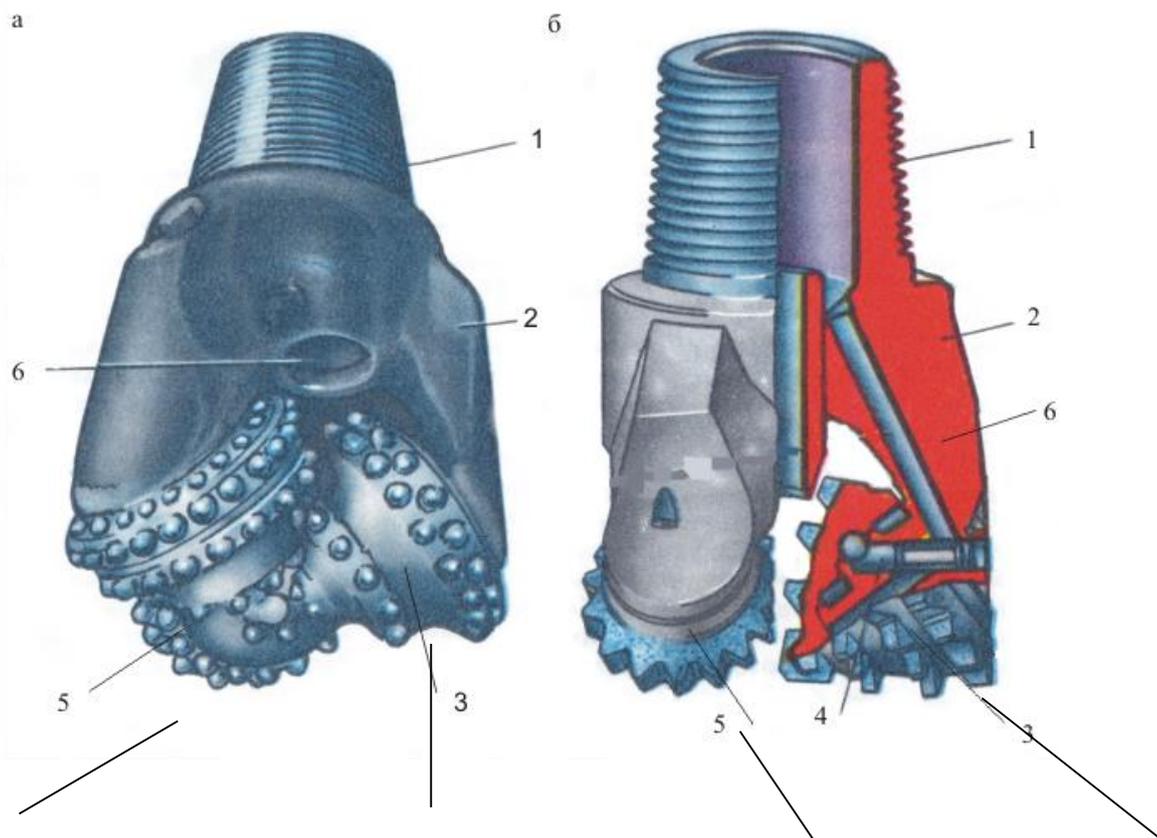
Трех шарошечное долото для бурения взрывных скважин с твердосплавными (а) и фрезерованными (б) зубками:
